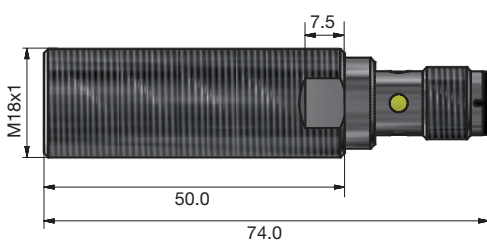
Lange Ausführung, bündiger Einbau, Steckversion
